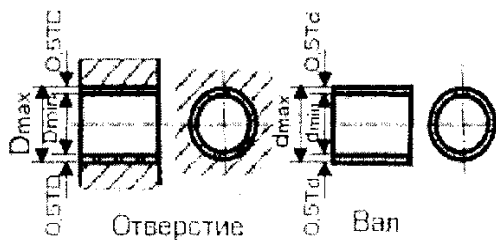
Положение допусков отверстия TD и вала Td
